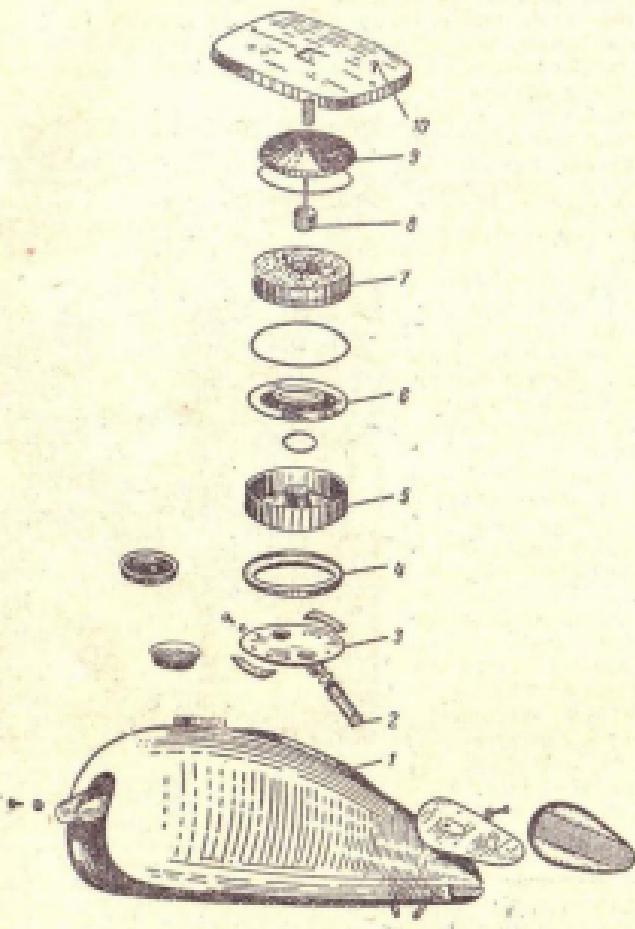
Детали воздухоочистителя, устанавливаемого в топливный бак:
